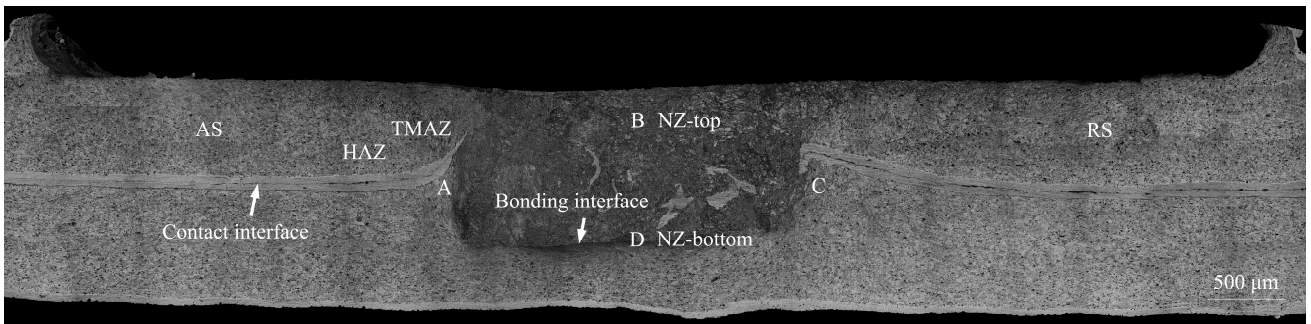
转速6000 r/min和焊速900 mm/min时2024铝合金FSLW接头宏观组织形貌
